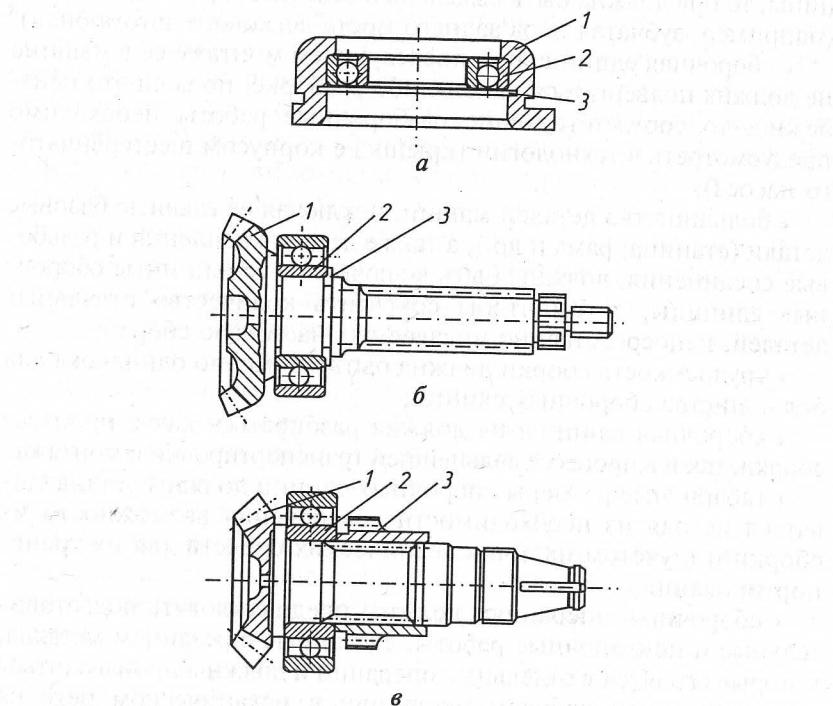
Сборочные единицы одновариантного комплектования: а — сборка подшипника с крышкой; б — сборка подшипника с валом-шестерней; в — сборка подшипника с валом-шестерней и шестерней
